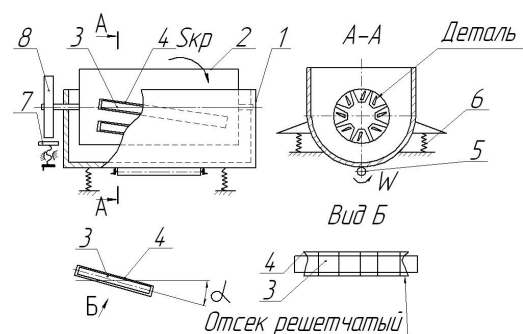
Технологическая схема виброударной упрочняющей обработки длинномерных деталей в свободном состоянии: 1 – рабочая камера; 2 – приспособление; 3 – обрабатываемая деталь; 4 – отсек решетчатый; 5 – вибратор; 6 – пружина спиральная; 7 – тормозной башмак; 8 – барабан приводной
